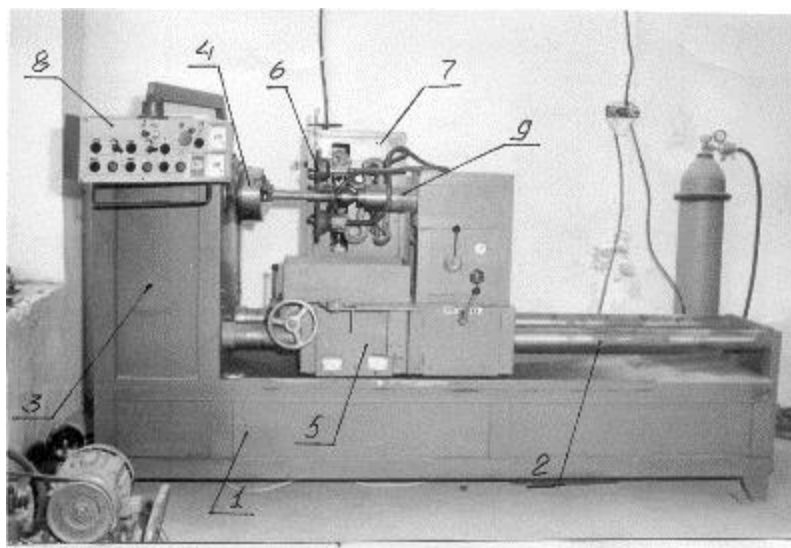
Общий вид установки 011-1-02Н «Ремдеталь» для
